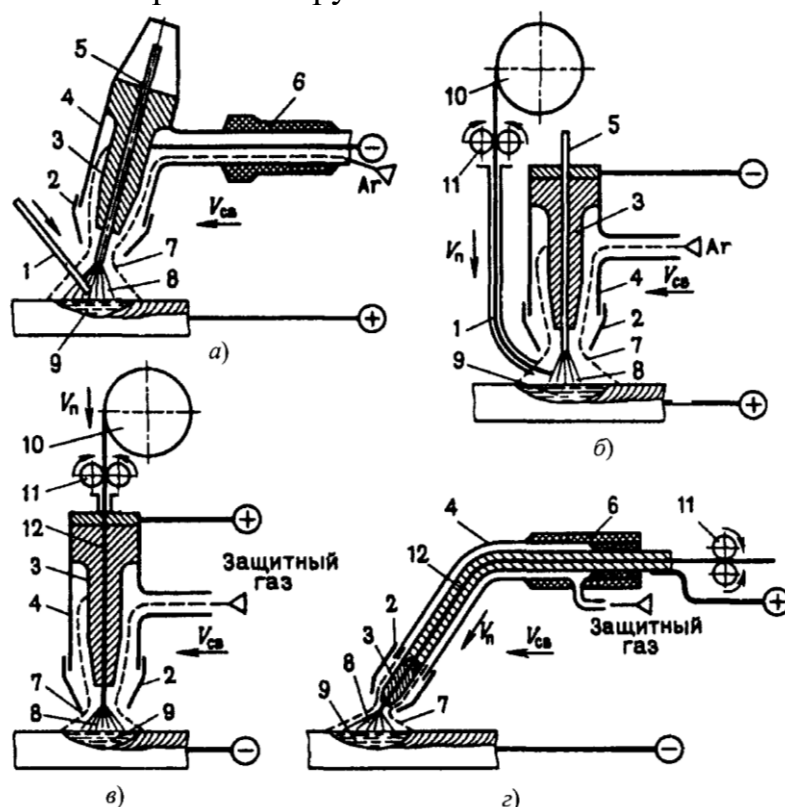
Виды сварки в защитных газах: 1 – присадочный пруток или проволока; 2 – сопло; 3 – токопроводящий мундштук; 4 – корпус горелки; 5 – неплавящийся вольфрамовый электрод; 6 – рукоять горелки; 7 – атмосфера защитного газа; 8 – сварочная дуга; 9 – ванна расплавленного металла; 10 – кассета с проволокой; 11 – механизм подачи; 12 – плавящийся металлический электрод (сварочная проволока)
